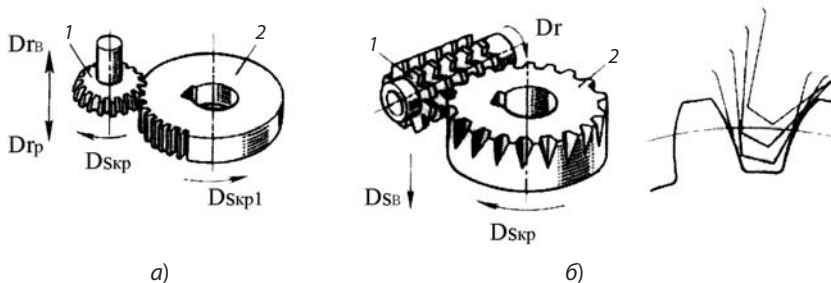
Примеры схем формообразования зубчатых колес:
